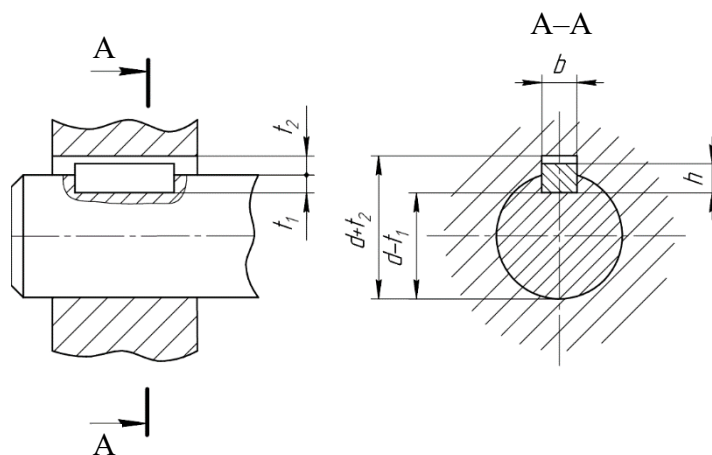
Обозначение основных геометрических параметров шпоночного соединения с призматической шпонкой
